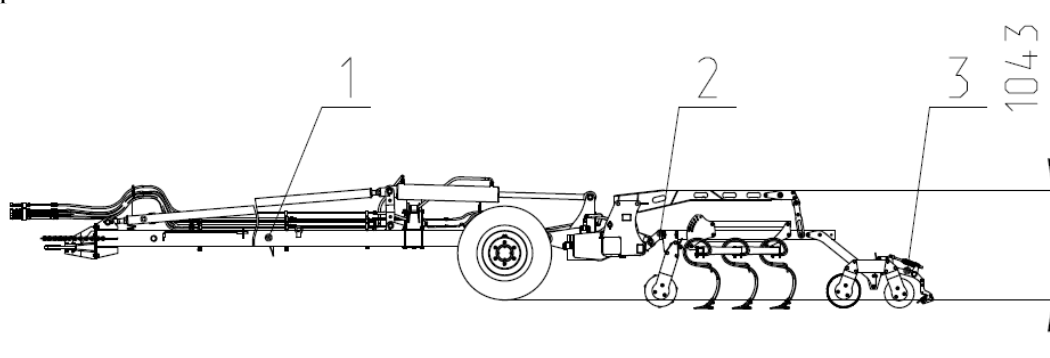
Культиватор КБП8-4 К1 "Орлан" (Вид сбоку)
